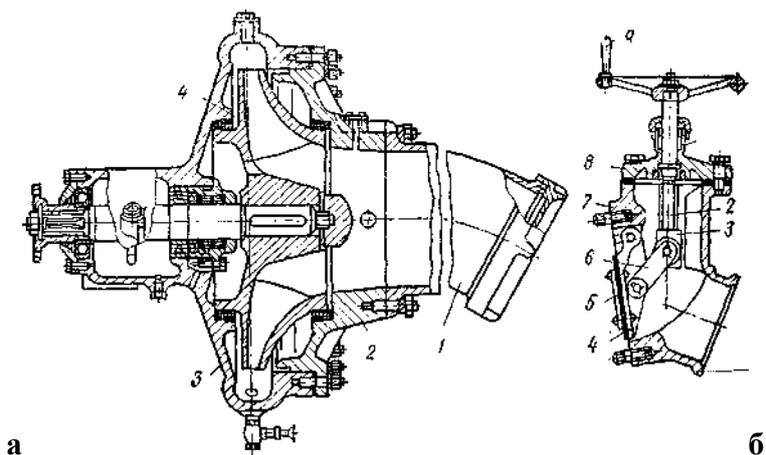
Пожарный насос ПН–110: а – продольный разрез: 1 – всасывающий патрубок; 2 – крышка; 3 – корпус; 4 – рабочее колесо; б – напорная задвижка: 1 – сальниковая набивка; 2 – шпindelь с резьбой; 3 – гайка; 4 – клапан с резиновой прокладкой; 5 – ось клапана; 6 – планка; 7 – корпус; 8 – крышка корпуса; 9 – маховичок
